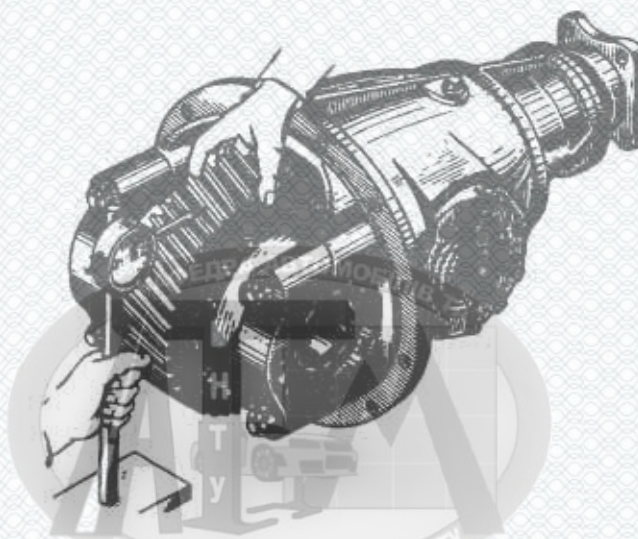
Перевірка зазору між зубами пари циліндричних шестерень за допомогою індикатора [10]
